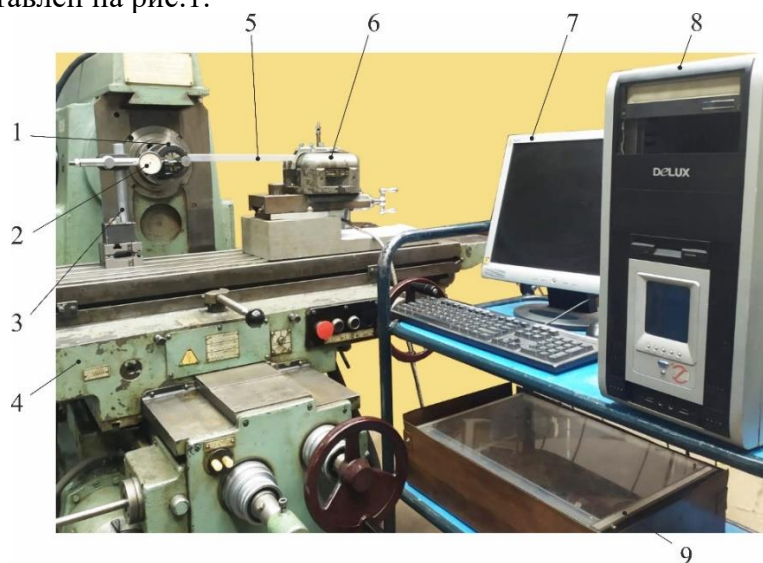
Общий вид установки: 1 - цанговый патрон; 2 - индикатор; 3 - стойка индикатора; 4 - стол станка; 5 - шток; 6 - динамометр УДМ-600; 7 - монитор; 8 - персональный компьютер; 9 - блок усиления и преобразования сигналов.
